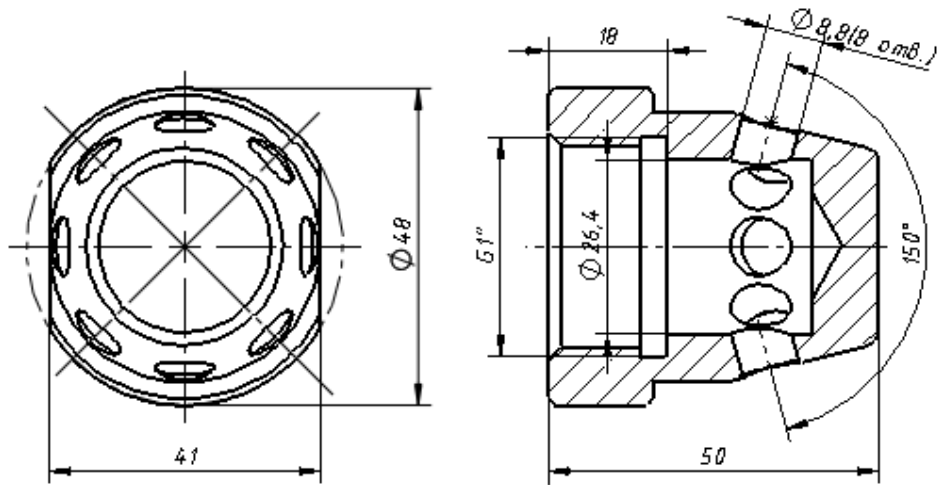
Общий вид распылителя РГ-Л-П-490-G1"
